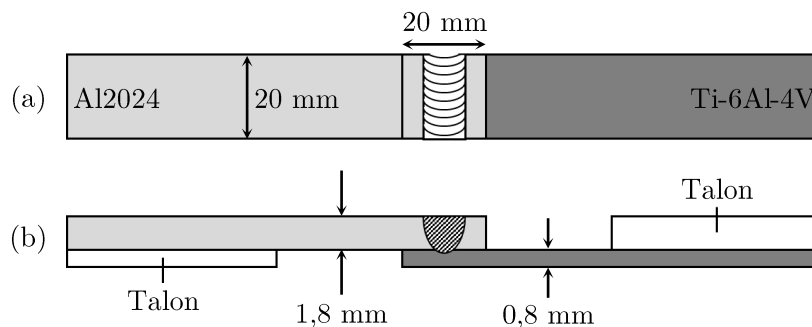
Dimensions des éprouvettes de traction-cisaillement : (a) vue du dessus et (b) vue en coupe transverse.
